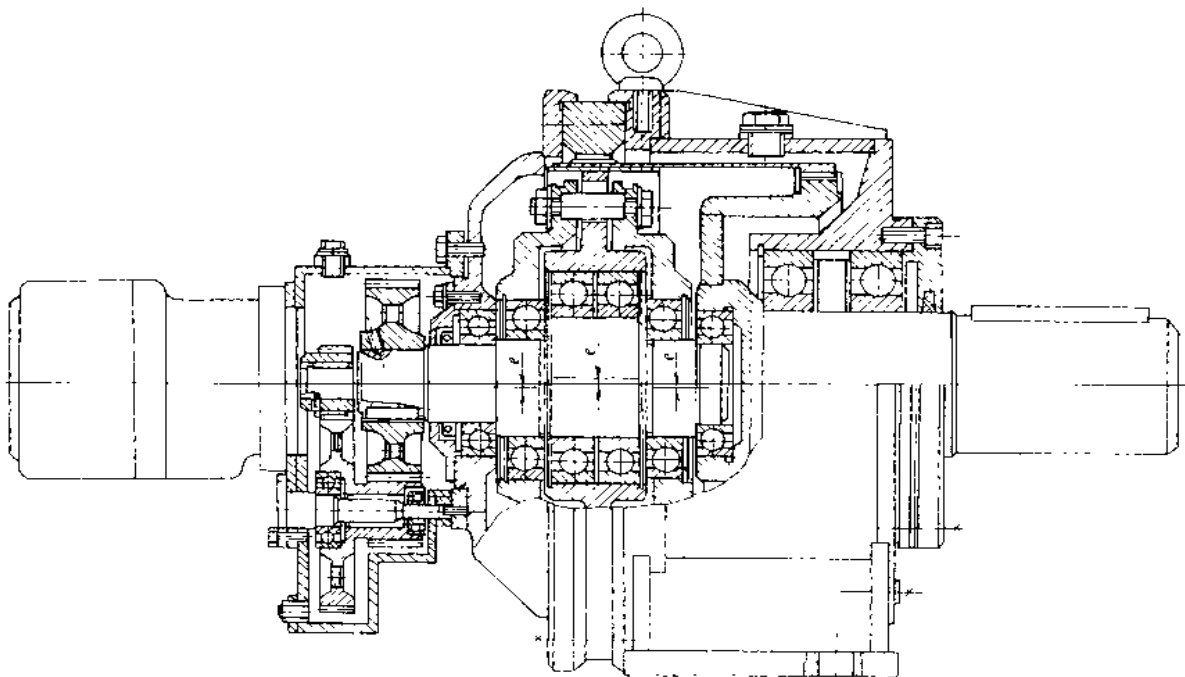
焊接管道用的旋转-定心器的减速器
